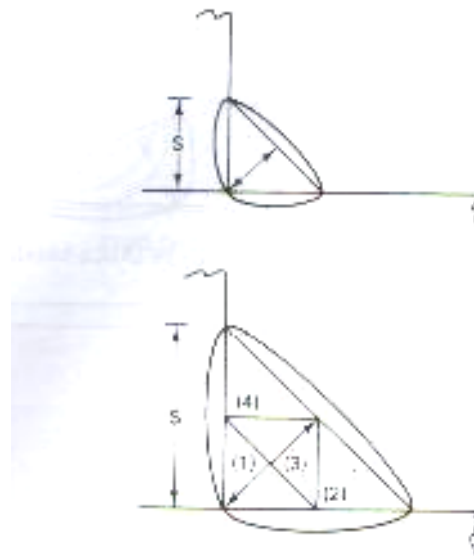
2. Tamaño contra resistencia de una soldadura de chaflán.
